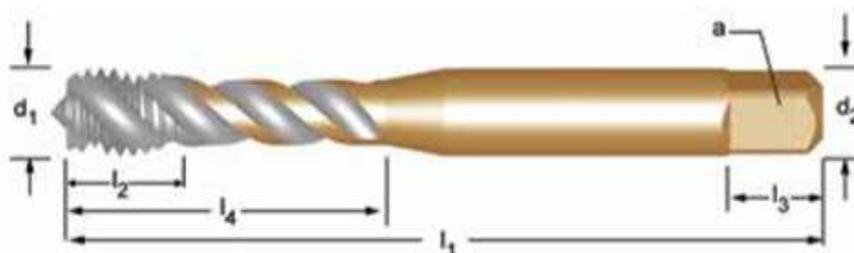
метчик для нарезания метрической резьбы ф. Dormer
